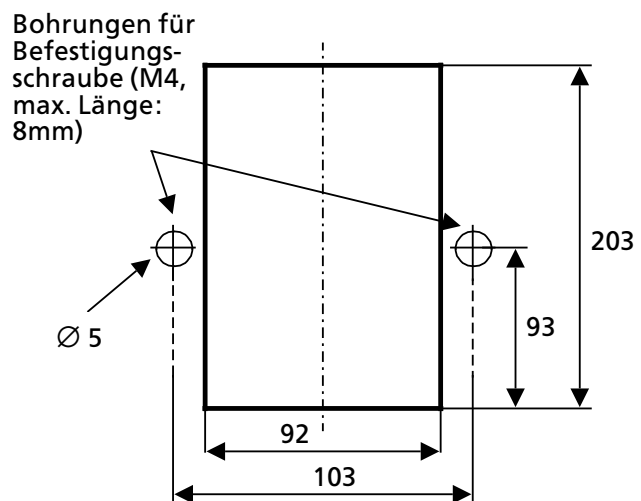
Ausschnittmaße (in mm) für Schalttafeleinbau
